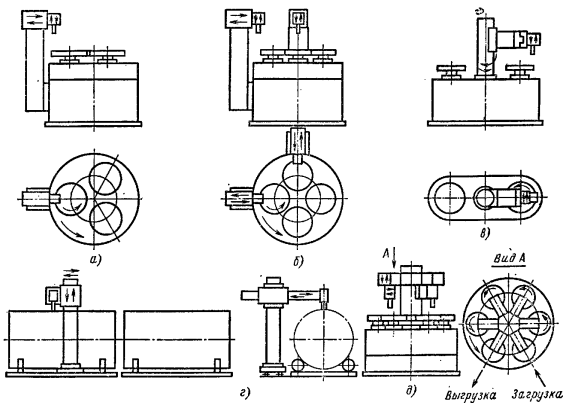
Типовые схемы компоновок многопозиционных установок и станков для электродуговой сварки круговых швов
